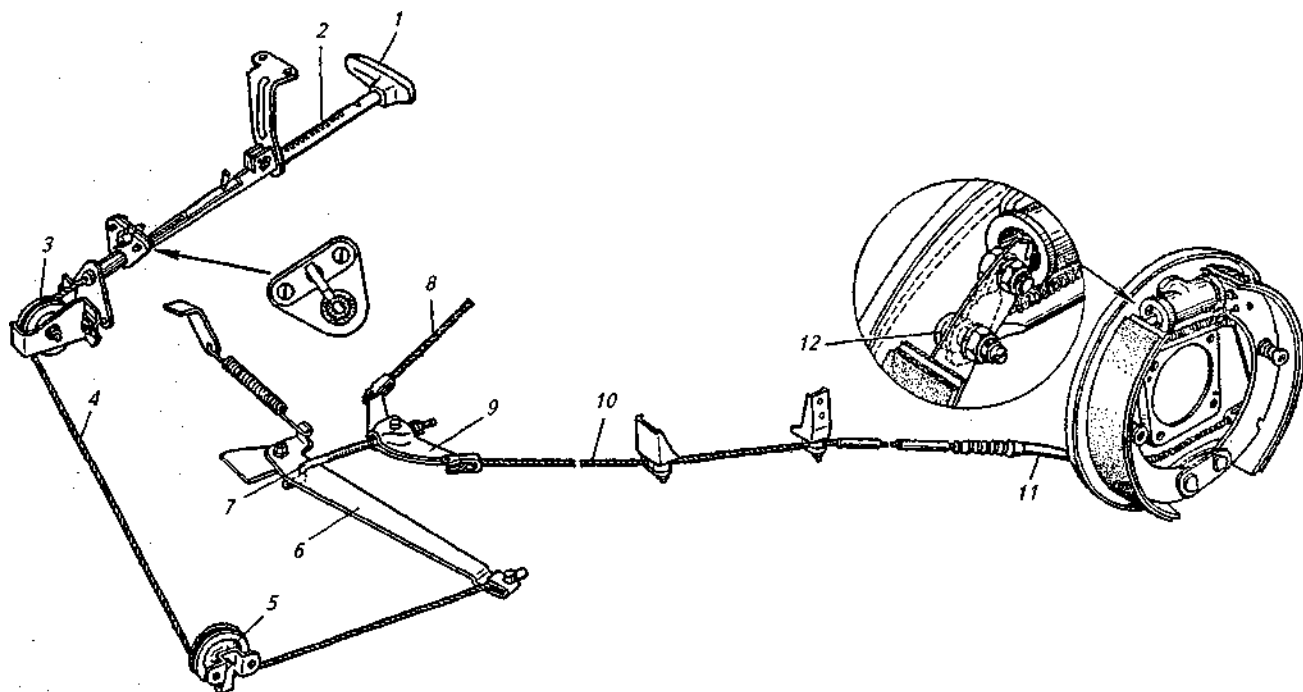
Стояночный тормоз, действующий на задние колеса: 1 – рукоятка; 2 – рычаг; 3,5 – ролики троса; 4 – передний трос; 6 – промежуточный рычаг; 7 – стержень; 8,10 – тросы привода тормозных механизмов; 9 – уравниватель тормоза; 11 – трубка; 12 – эксцентриковая ось разжимного рычага
